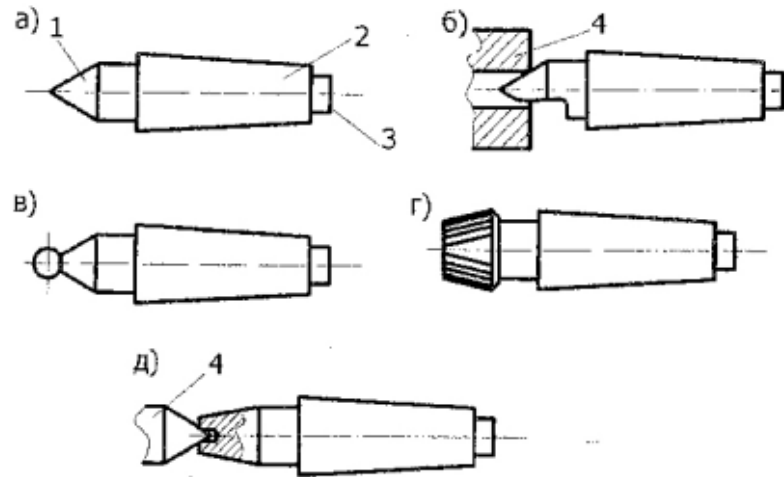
Основные конструкции центров: а – упорный (нормальный) центр; б – срезанный центр; в- шариковый центр; г – рифленый центр; д – обратный центр; 1 – рабочая часть; 2 – хвостовая часть; 3 – опорная часть; 4 – устанавливаемая заготовка.
